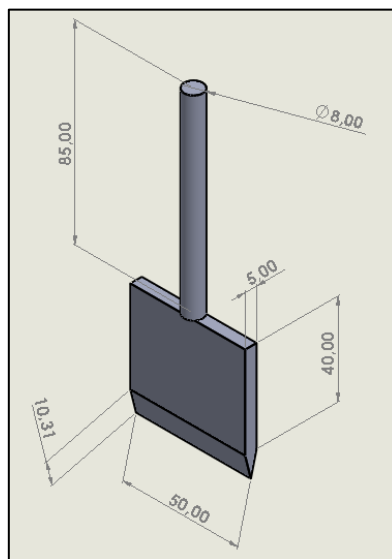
Dimensiones en (mm) - prototipo de cuchilla
